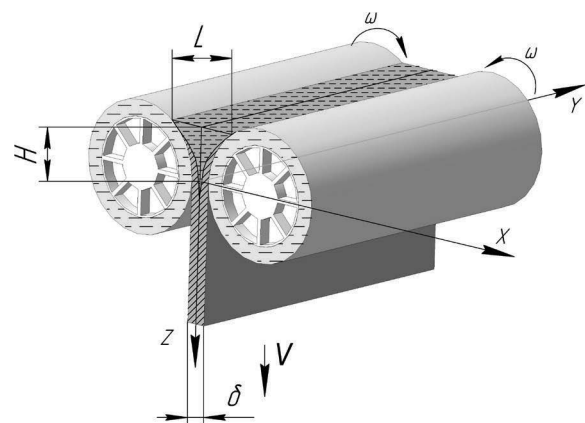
Валковый кристаллизатор и основные параметры разливки
